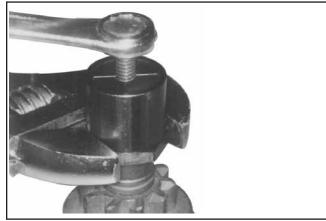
Werkzeug halten und Zentrumschraube im Uhrzeigersinn drehen, um den Haltering zu entfernen.
